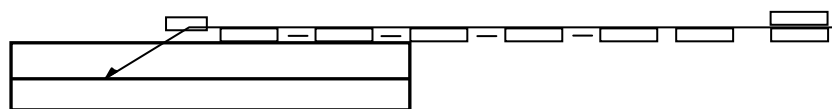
Обозначение сварного шва, выполняемого с невидимой стороны
